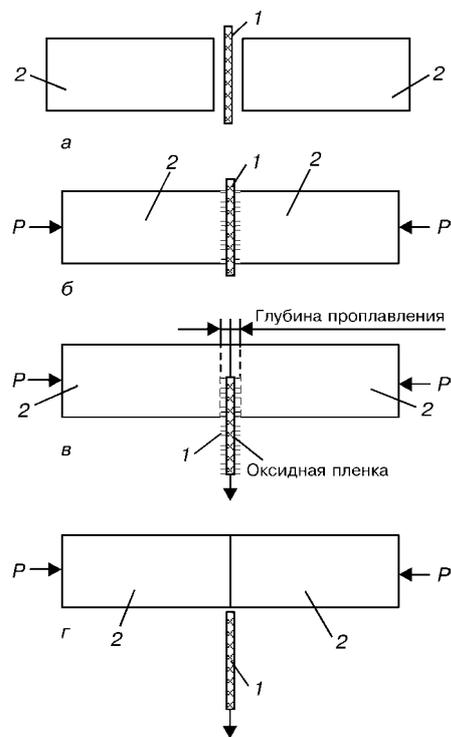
Схема последовательности процесса сварки термопластов с помощью ИК-излучателя (обозначения позиций см. в тексте)
